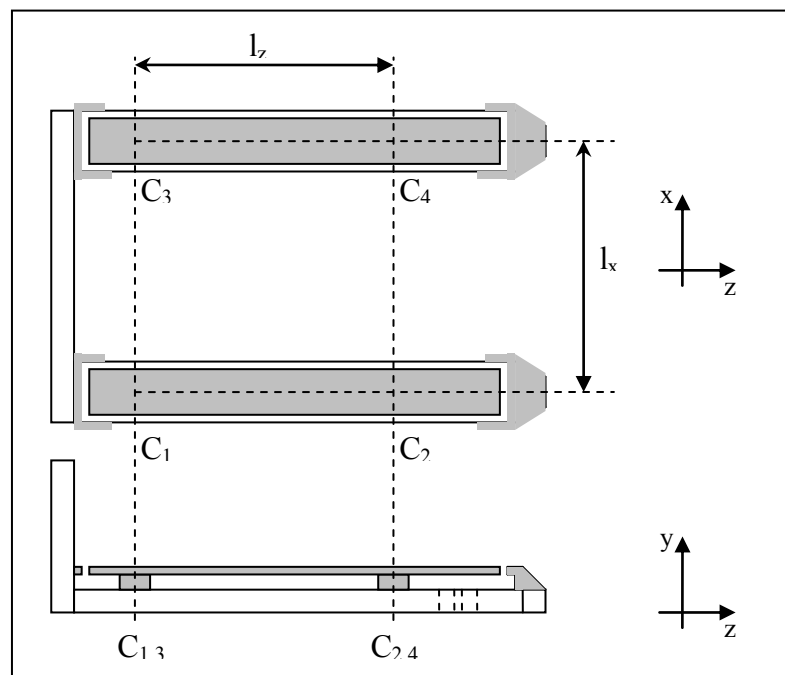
Schema della falsa forca (vista in pianta e laterale)
